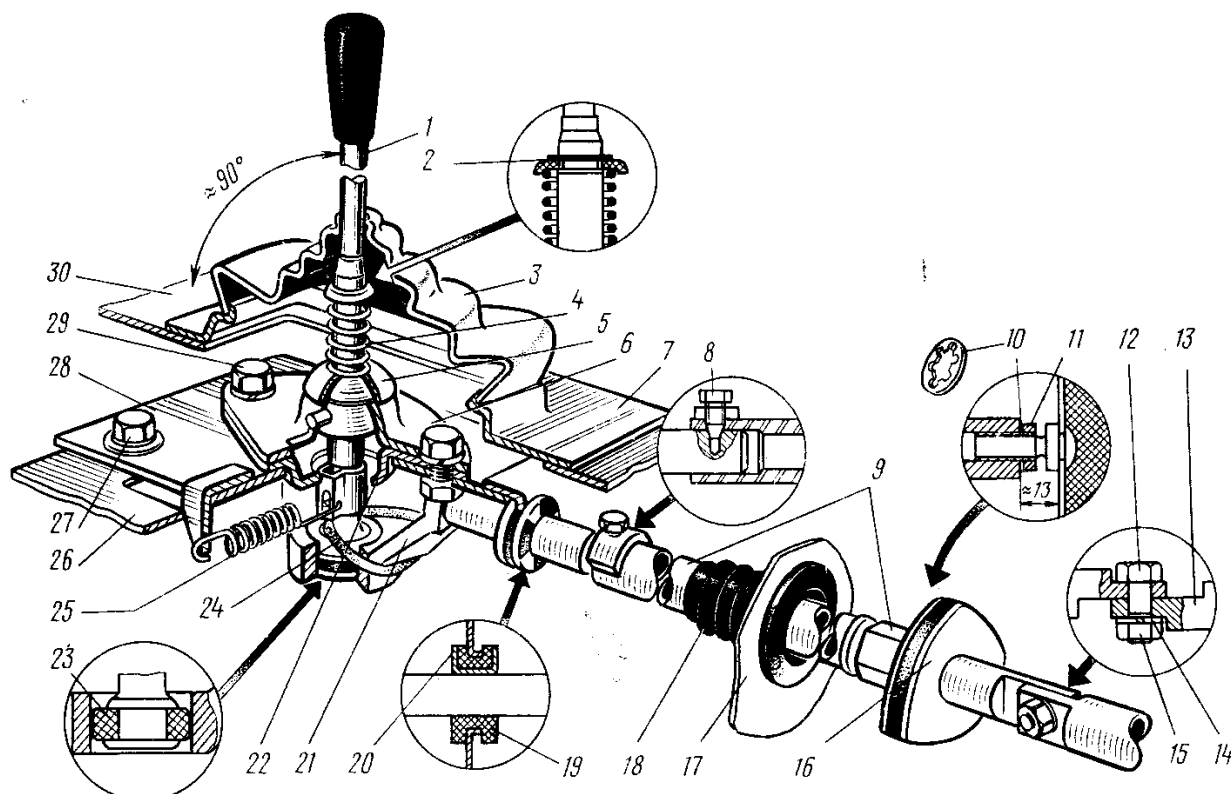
Механизм управления коробкой передач: 1 — рычаг; 2 — стопорное кольцо; 3 — кожух; 4 — пружина; 5 — упорная чашка; 6 — шаровая чашка; 7 — крышка; 8 — стопорный болт; 9 — вал; 10 — стопорная шайба; 11 — контргайка; 12 — специальный болт; 13 — ползун коробки передач; 14 — шайба; 15 — гайка; 16 — муфта; 17 — крышка туннеля пола; 18 — чехол; 19 — опорная втулка; 20 — вкладыш; 21 — ползун; 22 — направляющая чашка; 23 — демпфирующее кольцо; 24 — кольцо; 25 — пружина; 26 — кронштейн; 27 — болт крепления механизма; 28 — корпус; 29 — болт крепления чашки; 30 — туннель пола.
